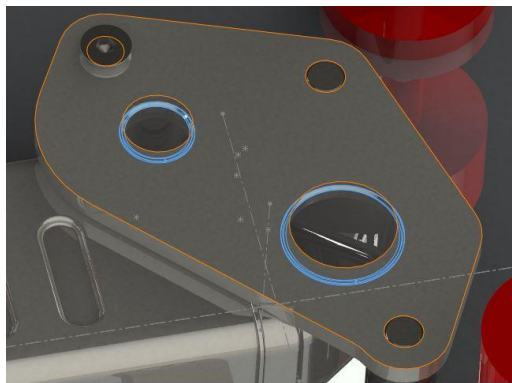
Zonas de soldadura láser en la brida de entrada de gases.
